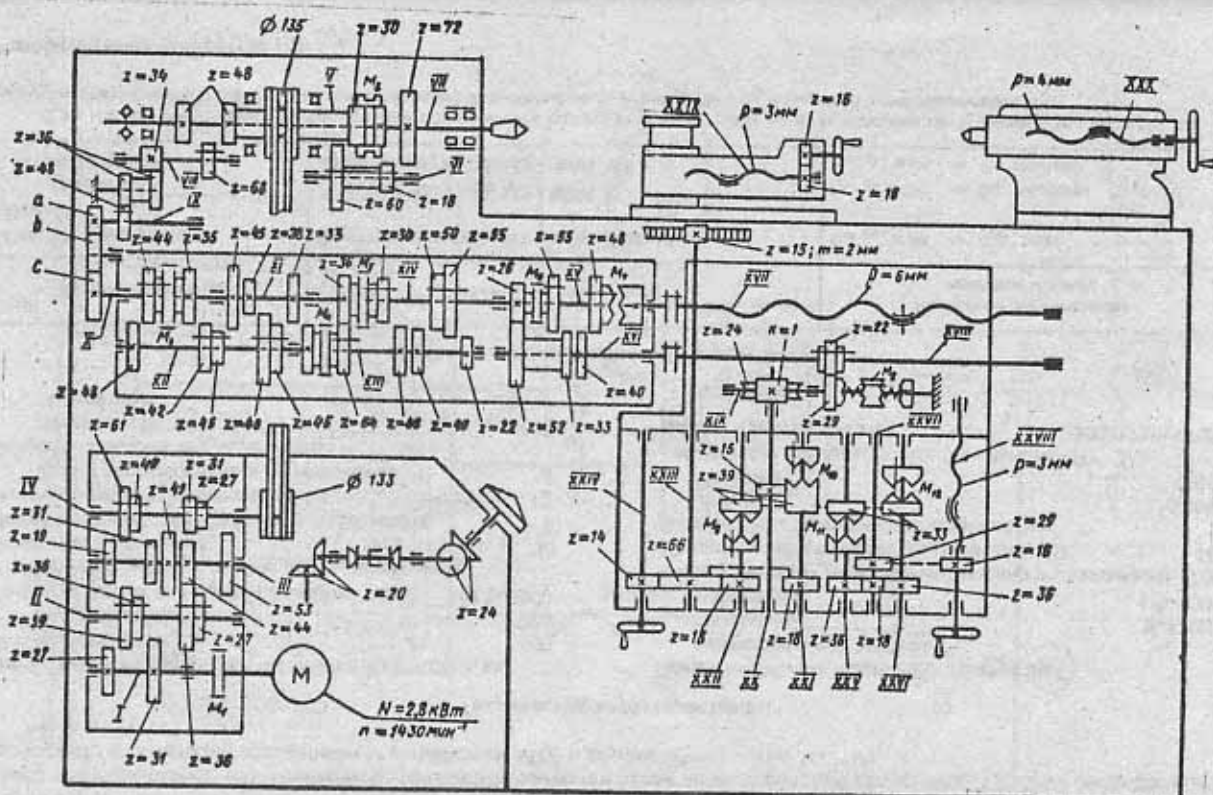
Кинематическая схема токарно-винторезного станка мод. 1И611П
